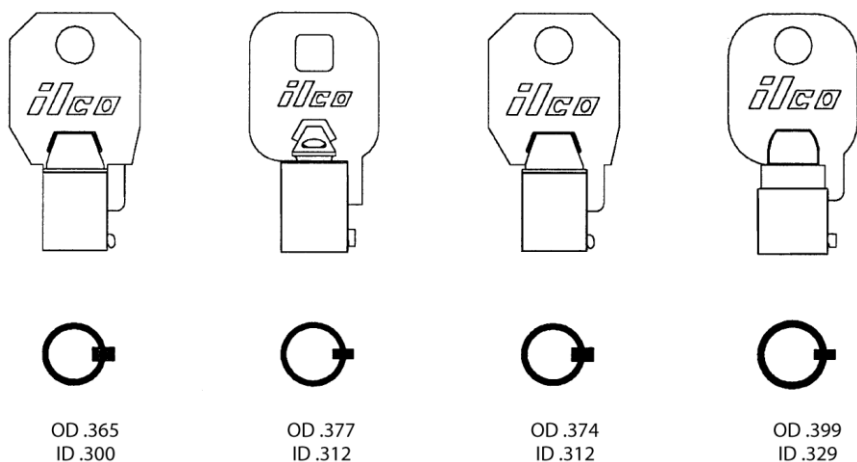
Заготовки трубчатого ключа, отличающиеся по размеру
